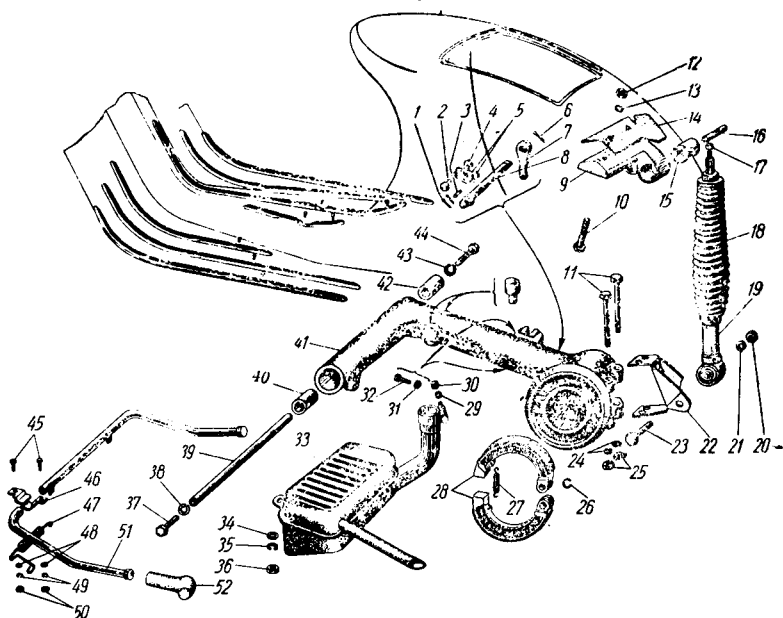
Подвеска заднего колеса, крепление глушителя, подставка мотороллера и настил пола:
